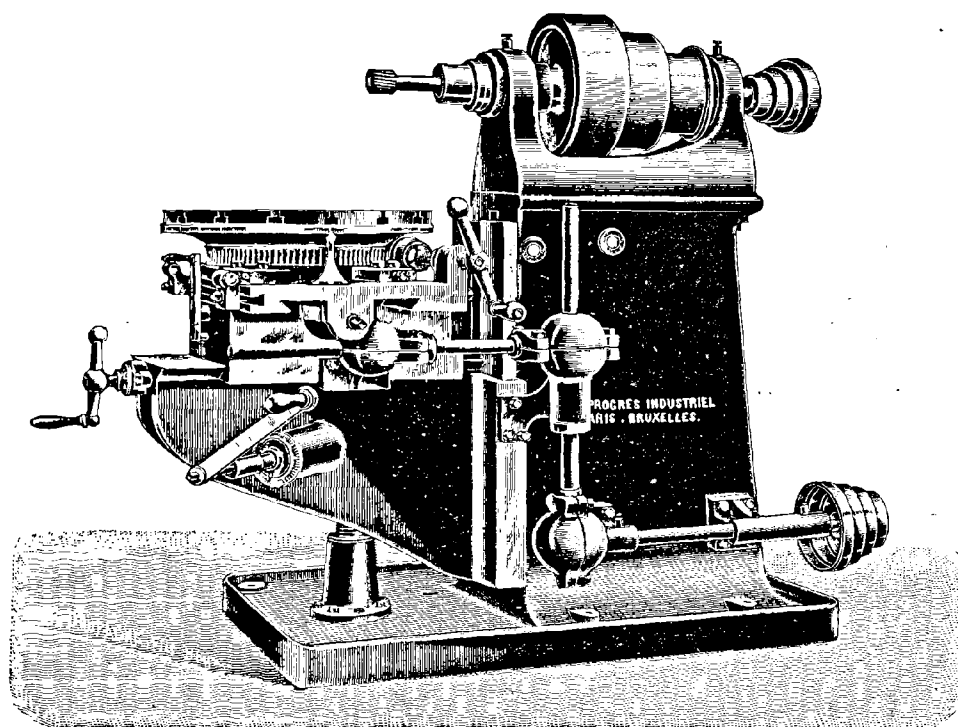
Machine à fraiser horizontale à plateau circulaire du Progrès Industriel.
